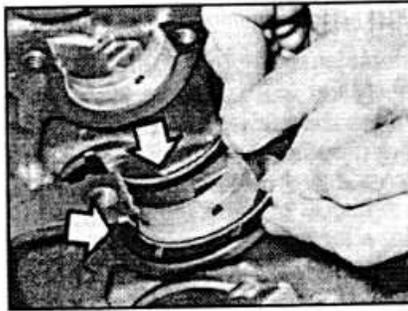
Е.32. Установка упорных полуколец коленчатого вала.
